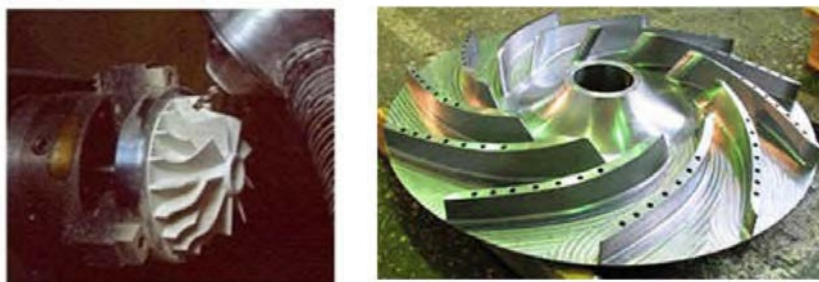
Дефекты на поверхностях деталей после фрезерования
